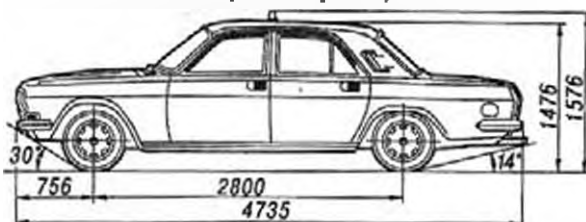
Автомобиль ГАЗ-24-11 "Волга" и его габаритные размеры
